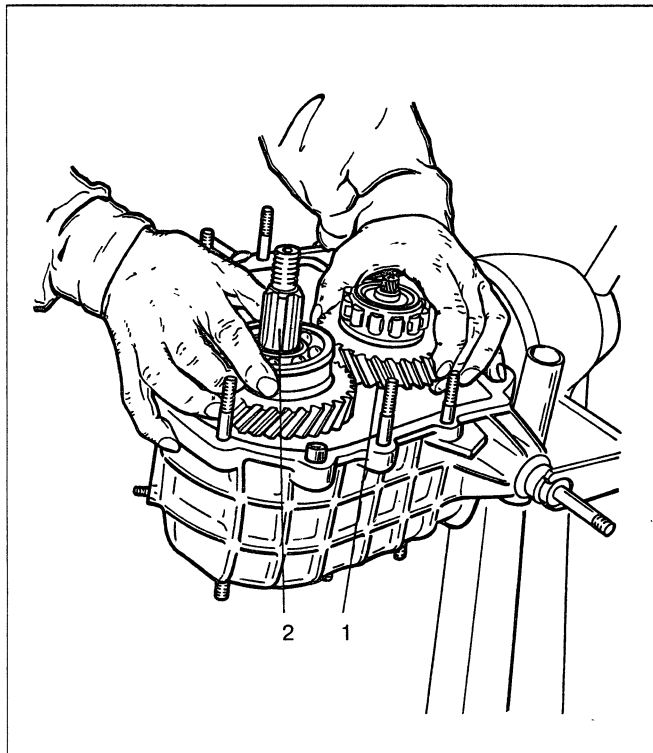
Установка в картер ведущего и промежуточного валов: 1 – промежуточный вал; 2 – ведущий вал
